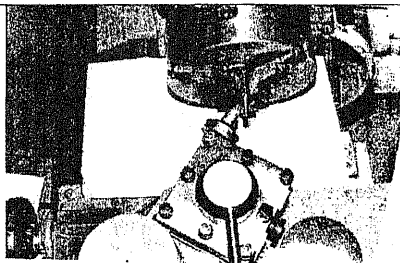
Настройка токарного станка для алмазного выглаживания конусного участка поверхности круглого резца
